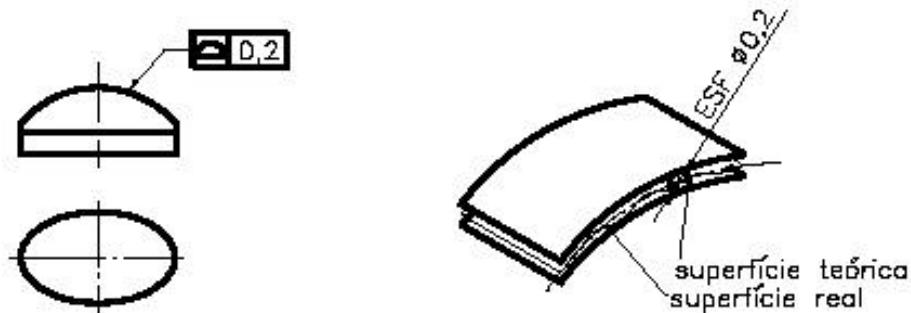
Tolerância de forma de superfície – especificação em desenho e interpretação.
